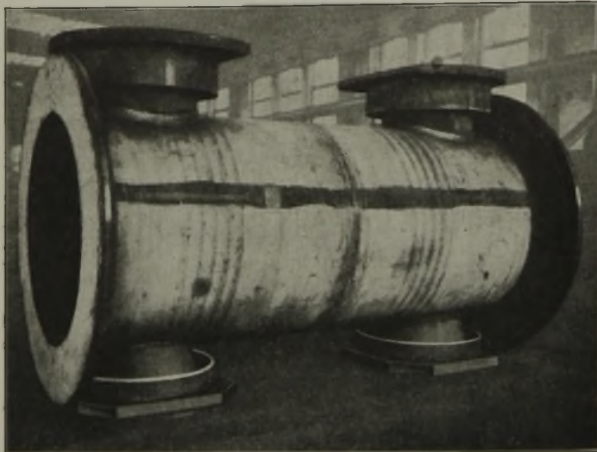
Innerer Zylindermantel verschweißt mit den Stirnflanschen und Ventilkammern.
